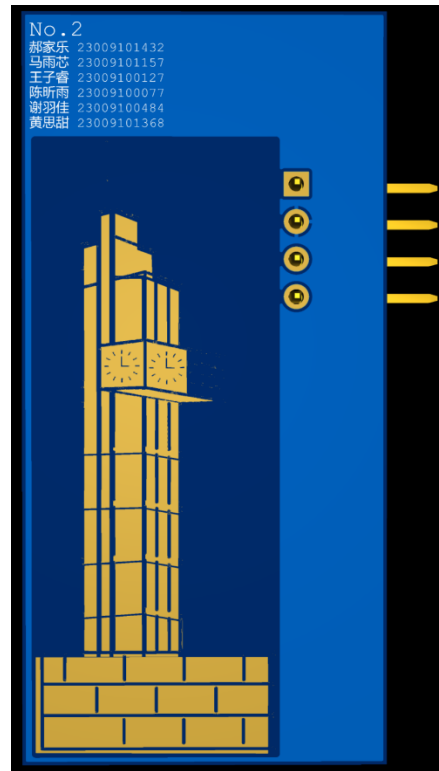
8 位流水灯 PCB 底层 3D 外壳预览图
